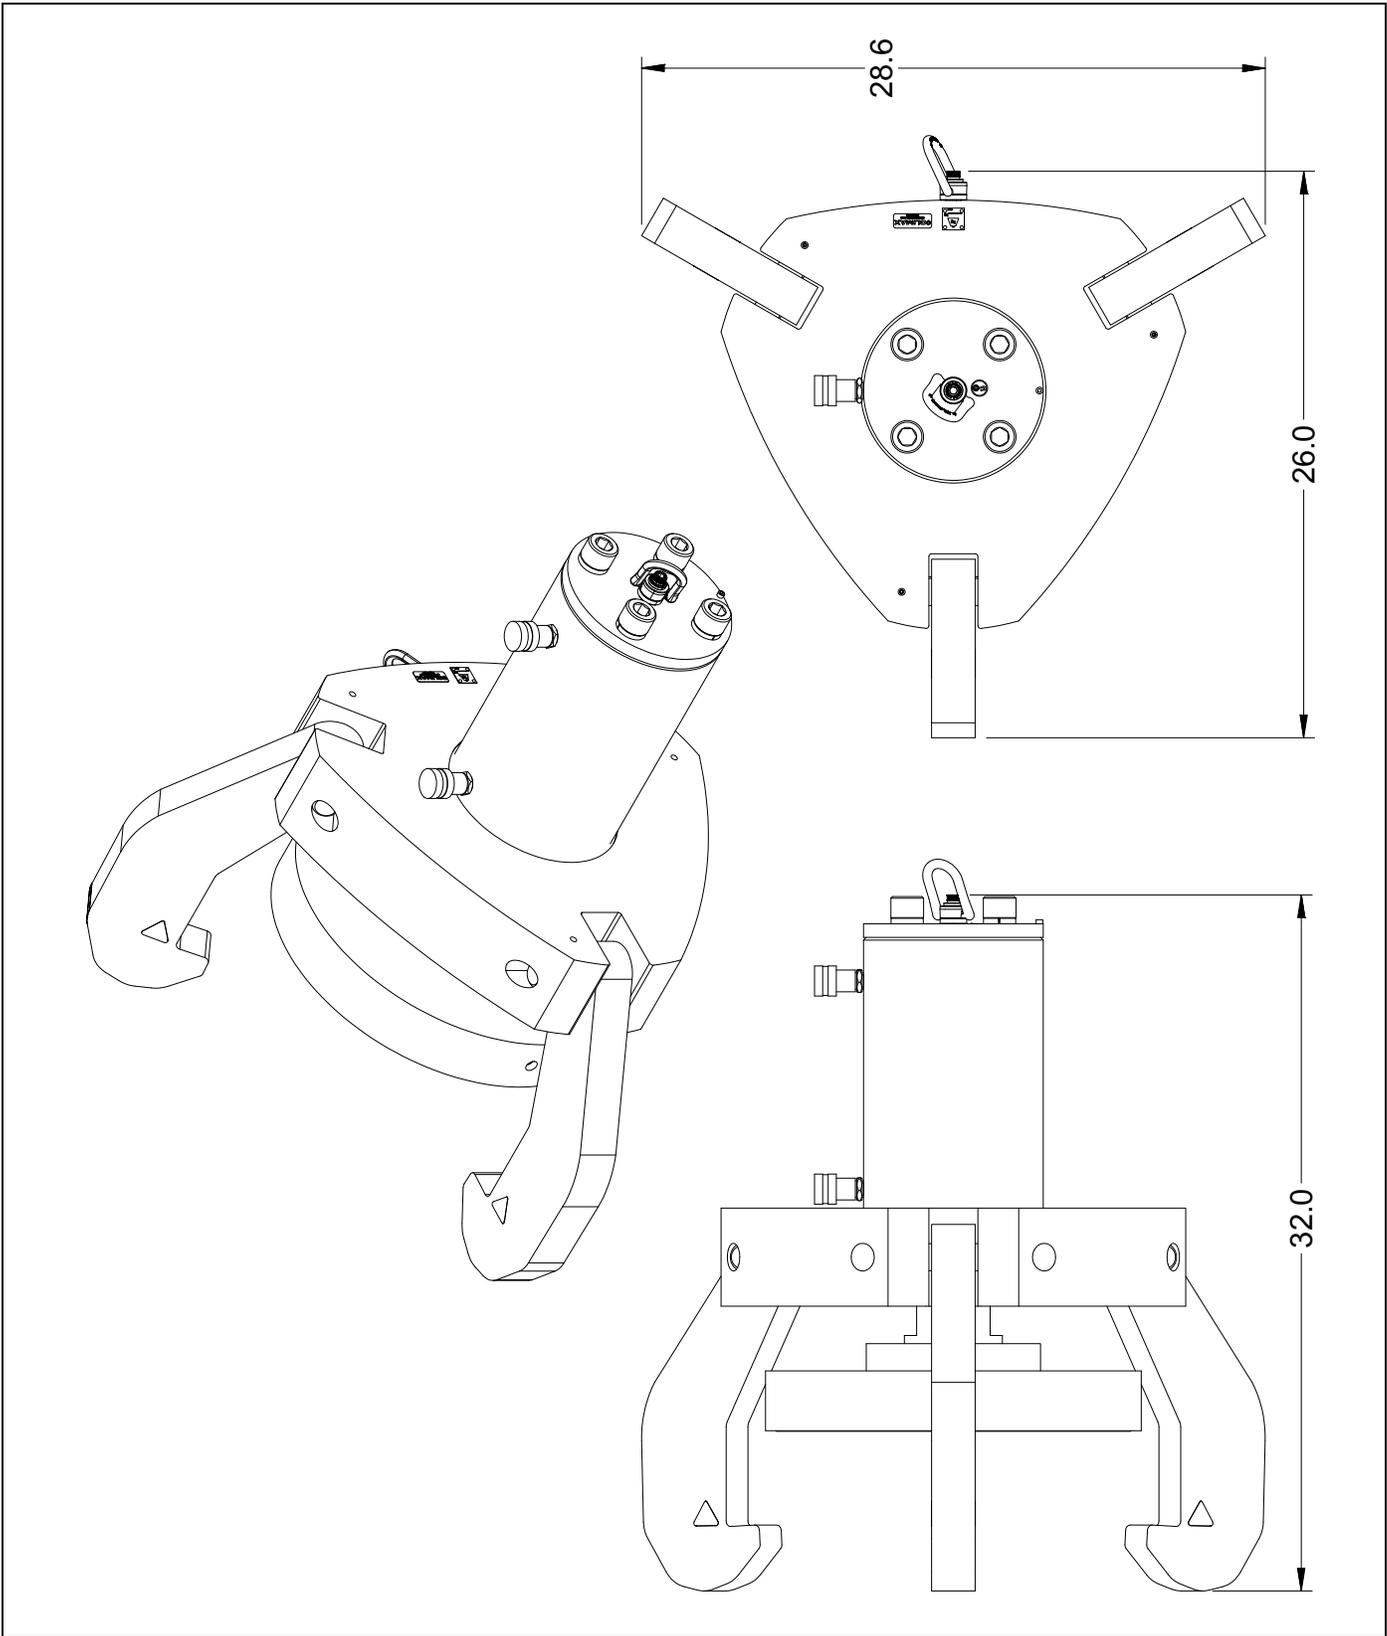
DIMENSIONS DE LA HFS-16
